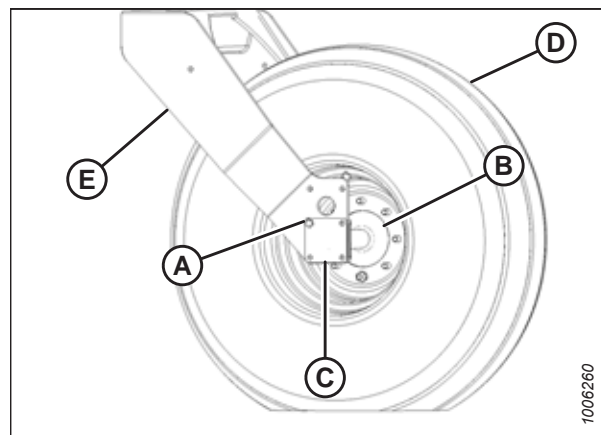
Вилочное самоустанавливающееся колесо
